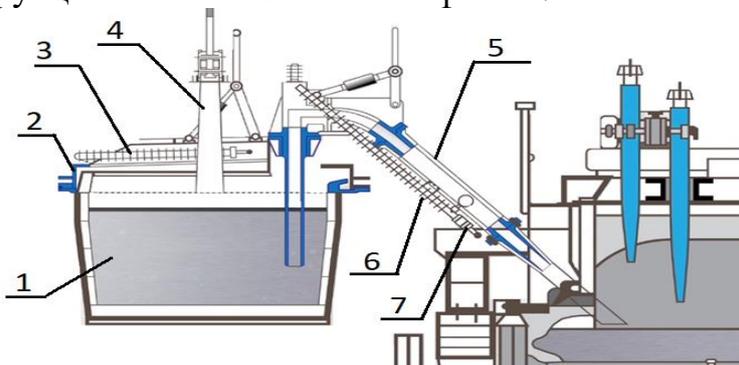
Вакуум-транспортный ковш со съёмным сифоном. 1 – Стальной корпус; 2 – футерованная огнеупорным кирпичом крышка с жаровой трубой; 3 – грузоподъемная траверса. 4 – съёмный сифон; 5 сливная труба; 6 вторая жаровая труба, 7 – с запирающее устройство.
